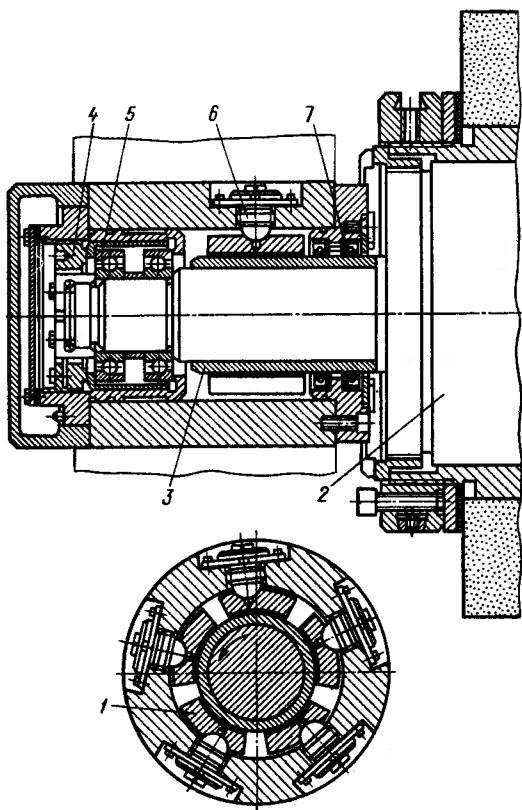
Опора шпинделя шлифовального круга с гидродинамическим пятикладышным подшипником
